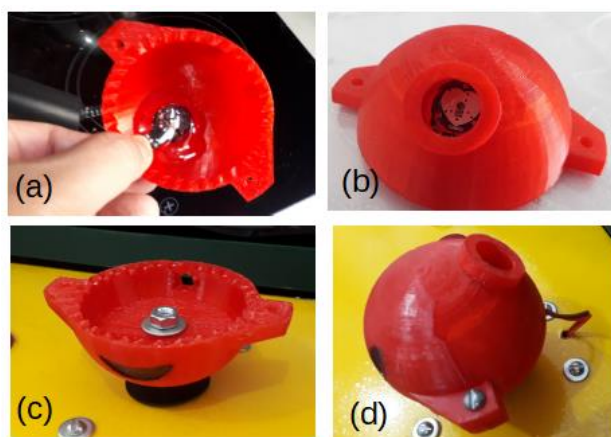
(a) Fixação do sensor no interior da empunhadura, (b) Vista externa do sensor, (c) Encaixe mecânico no eixo do joystick e (d) Passagem de fios do sensor para o interior do gabinete.
